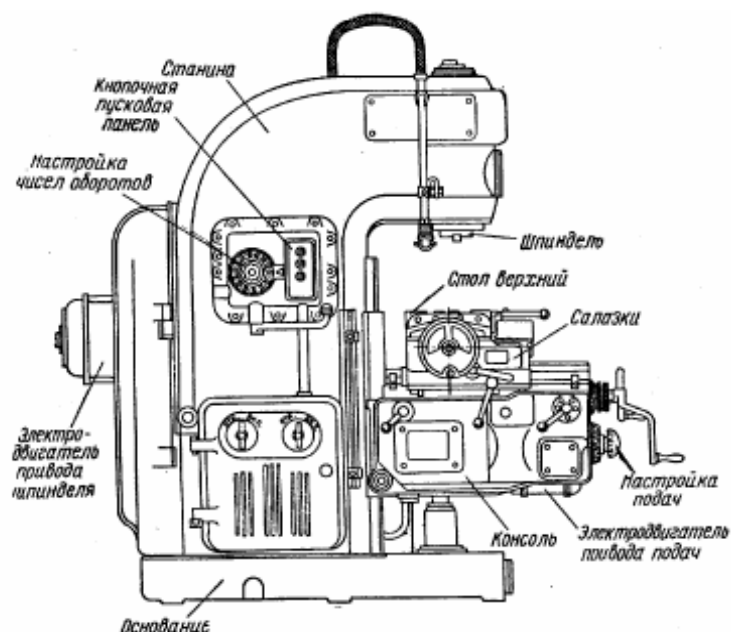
Вертикально-фрезерный станок 6Н12
